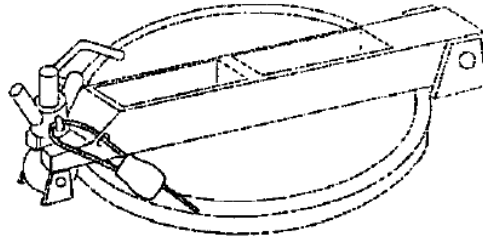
Схема установки универсального ЗПУ с длиной каната 300 мм на верхней крышке загрузочного люка цистерны ригельного типа при наличии пломбировочных проушин
